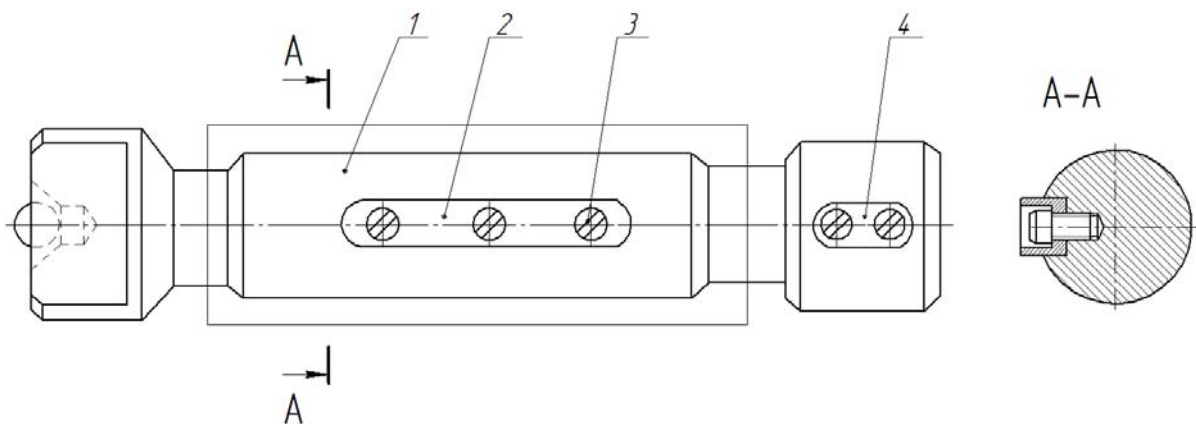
Будова гладкої оправки зі шпонкою: 1 – оправка; 2 – основна шпонка; 3 – гвинт; 4 – напрямна шпонка
